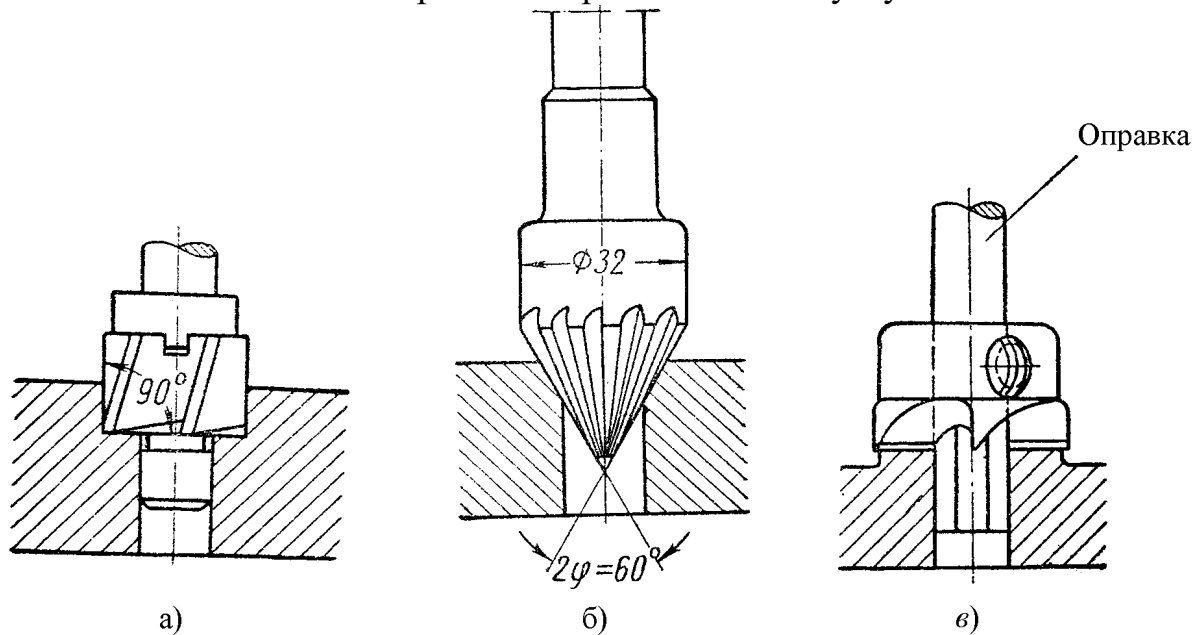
Зенковки: а – для цилиндрических гнезд; б – коническая; в – торцовый зенкер – цековка.
